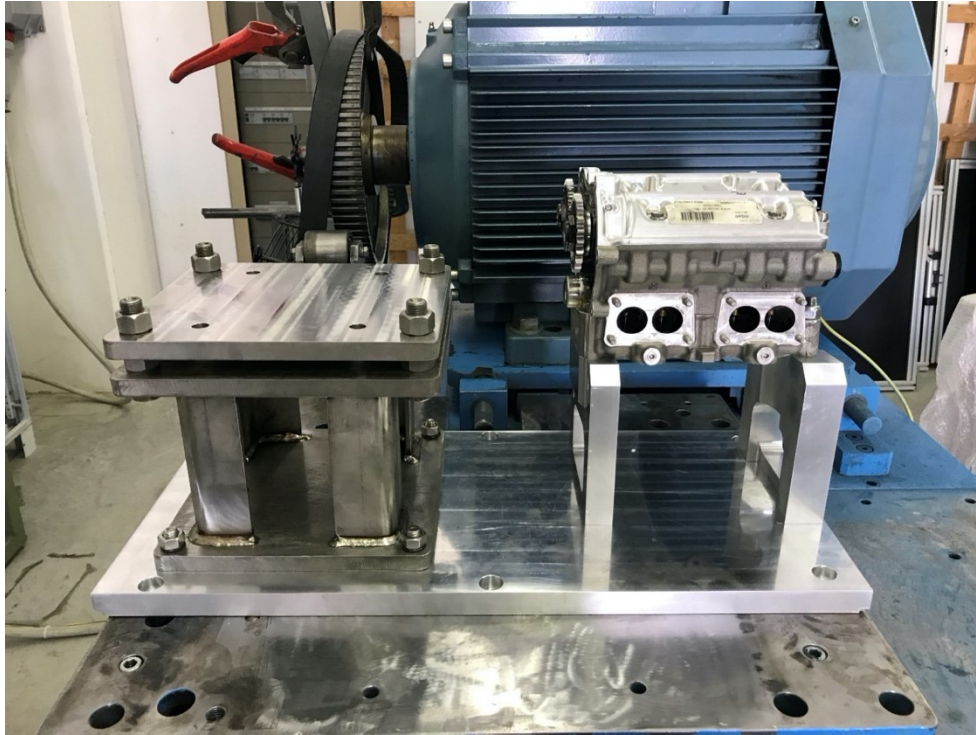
assemblaggio testata su supporti e castello di supporto trasmissione; il tutto è fissato sulla piastra rettificata in alluminio
